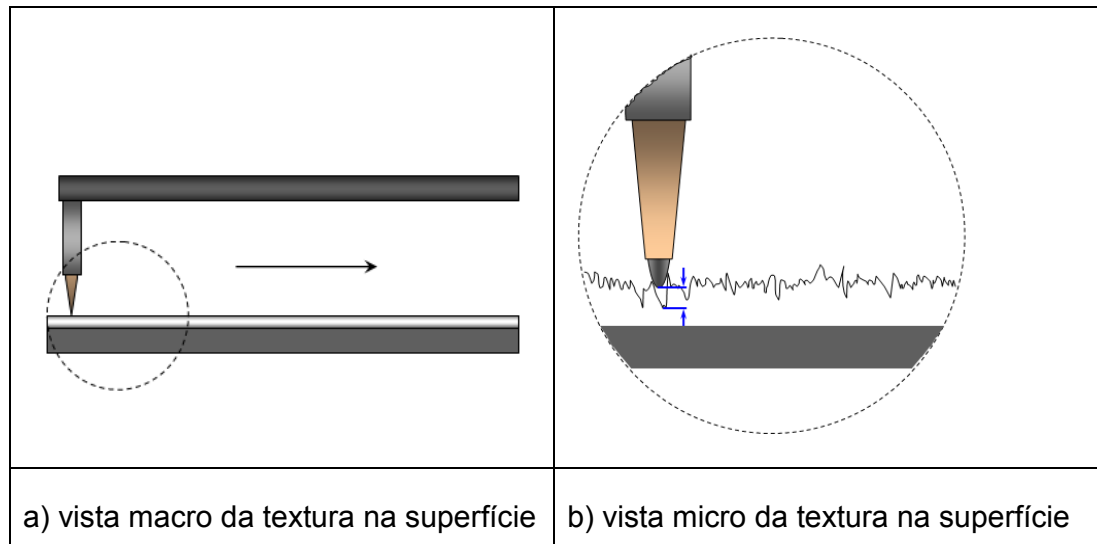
Ponta do apalpador sobre a superfície com duas vistas.
